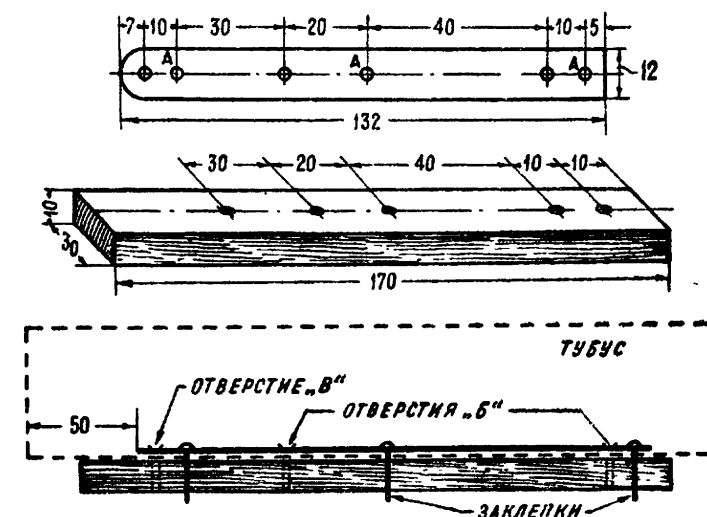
Подвижная пластинка, пластинка крепления тубуса и схема крепления тубуса
